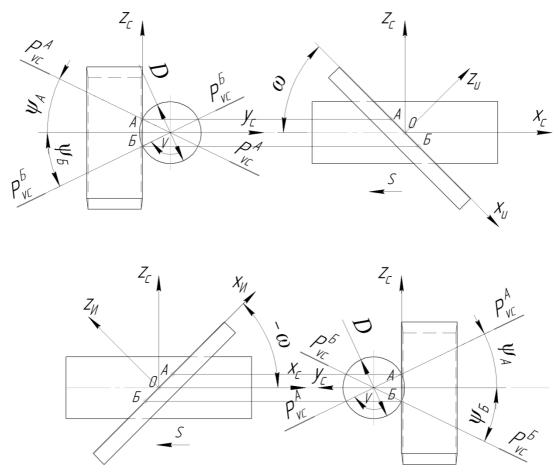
Схема процесса безвершинного точения с ориентацией осей инструментальной и статической систем координат [6]
